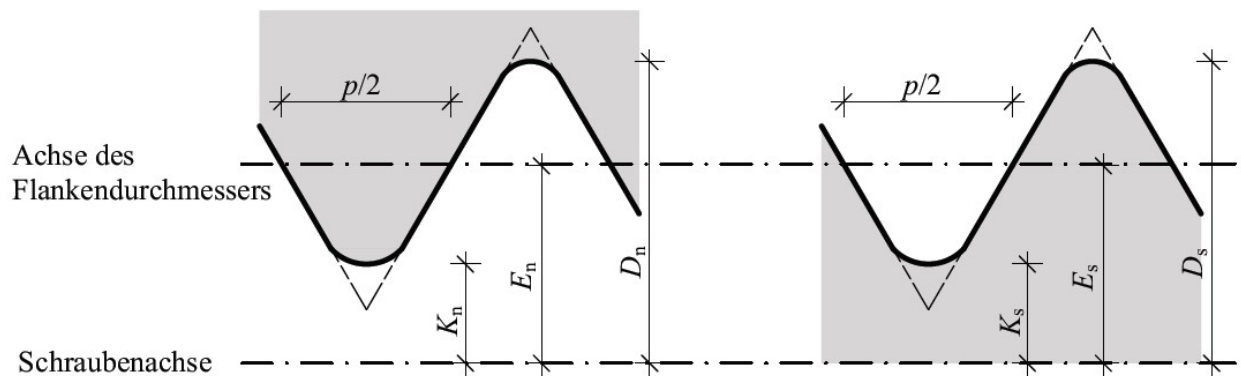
(links) Innengewinde; (rechts) Außengewinde (Machinery's Handbook 2008)
